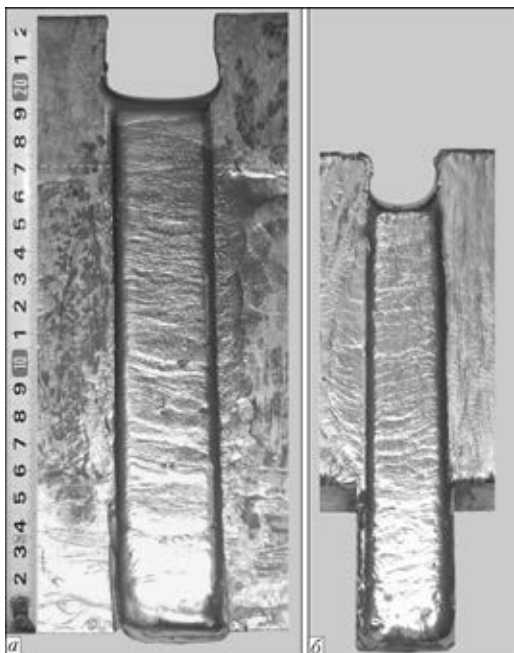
Боковые поверхности сварных соединений, выполненных стандартной ЭШС (а) и ЭШС в узкий зазор (б)
